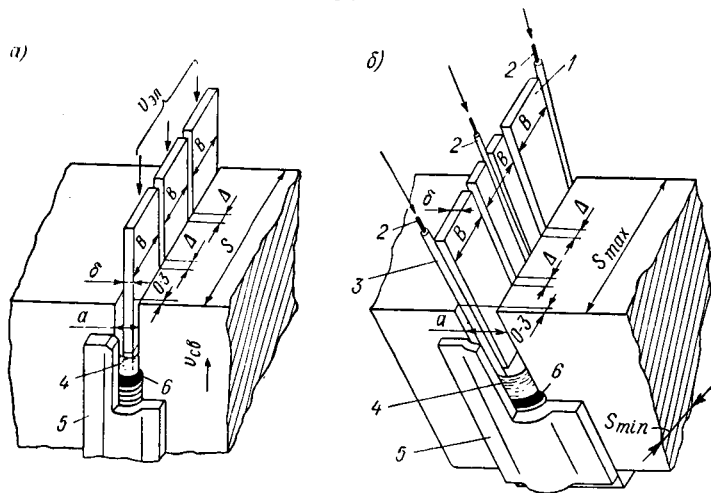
Пластинчатые и пластино-проволочные электроды электрошлаковой сварки: а — электрошлаковая сварка пластинчатыми электродами; б — электрошлаковая сварка пластино-проволочными электродами;
